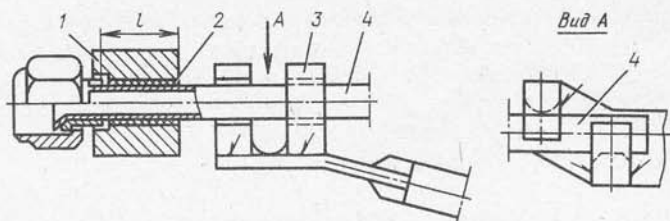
3. Схема подгибки трубопроводов в местах их соединения и в зоне крепления: 1 – быстроразъемная оправка; 2 – фторопластовая прокладка; 3 – приспособление для подгибки трубопроводов; 4 – трубопровод
